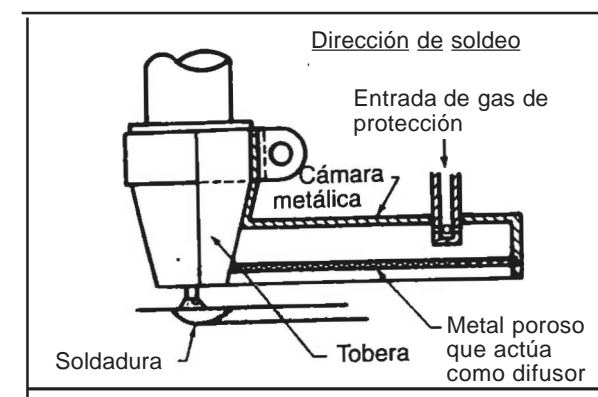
CÁMARA REMOLCADA PARA SOLDEO DE TITANIO
